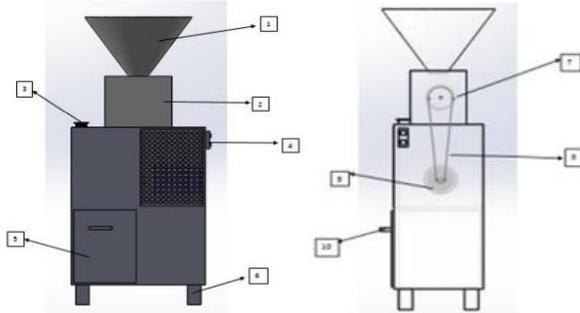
Conjunto de componentes (Diseño realizado por los autores).
